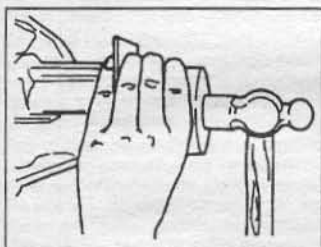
Установка сальника ведущей шестерни главной передачи.
